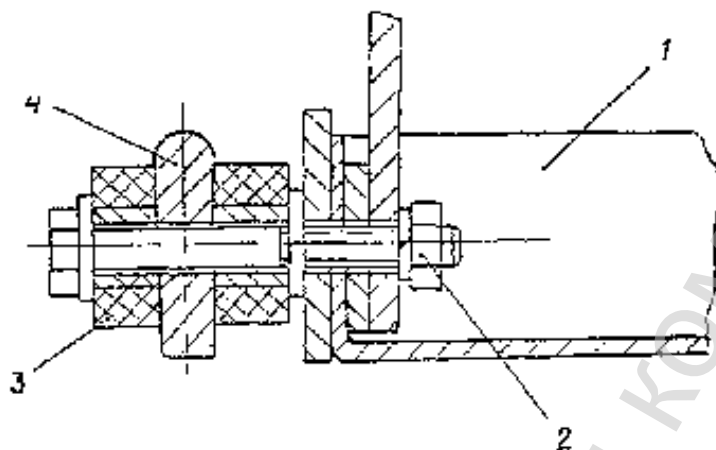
Крепление направляющей линейки к потолочному щиту по оси кабины:
